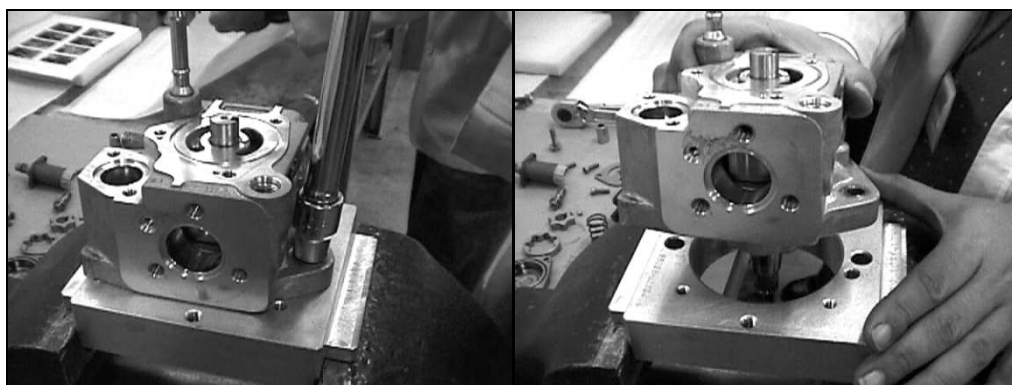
Extracción del conjunto de la placa de la bomba.
